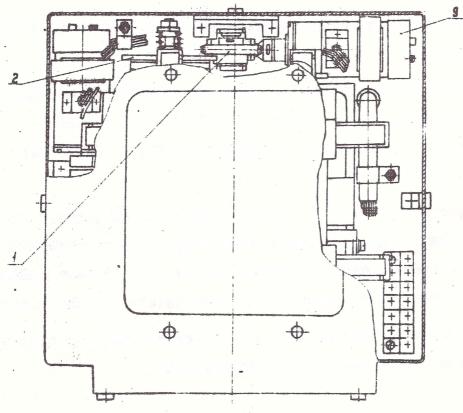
1-Редунтор: 2-Нуфта: 3- Упор; 4-Кечтия, 5-Шторка; 6-Шторка; 7-Шторка; 8-Болт, 9-Электоодвигатель
